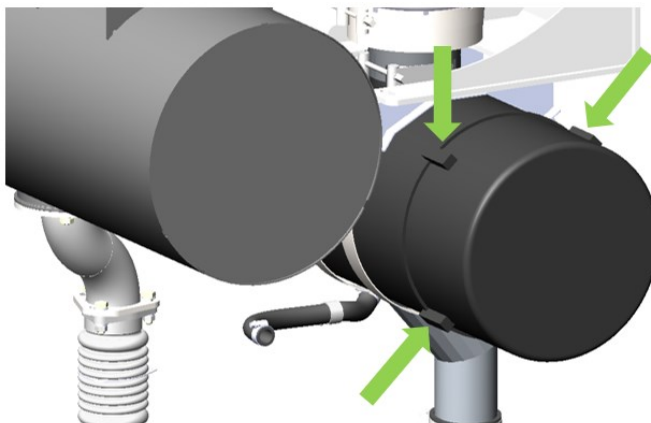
Корпус воздушного фильтра Тип 1
